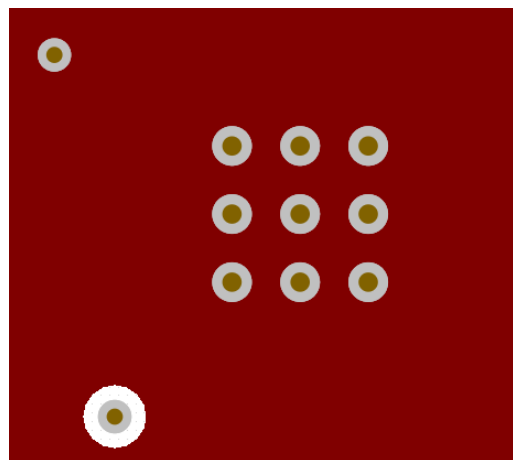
LMK1D2104L 的 PCB 布局示例，GND 层
